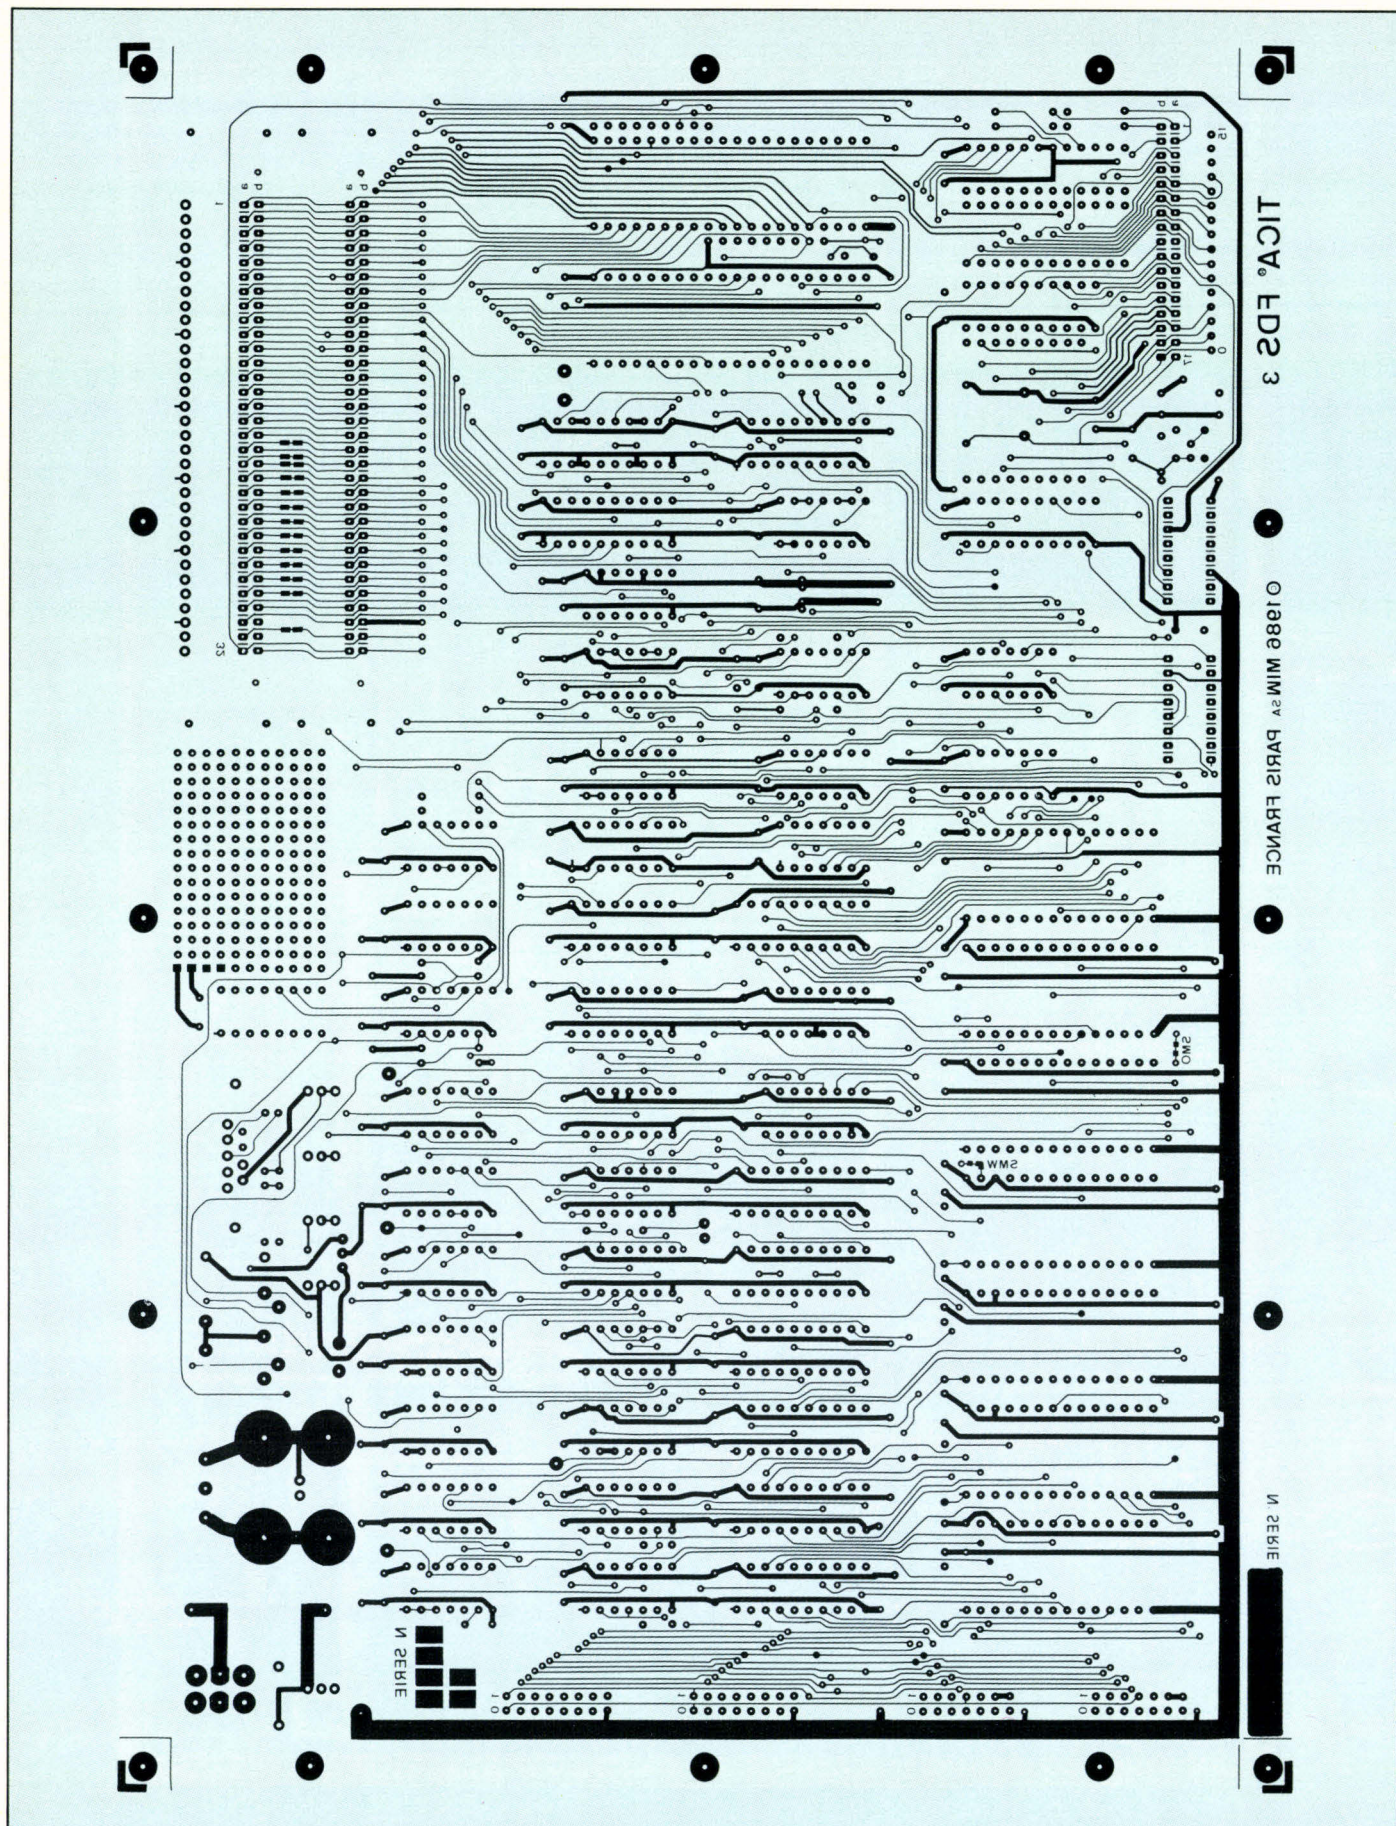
Circuit imprimé vu côté soudures.
